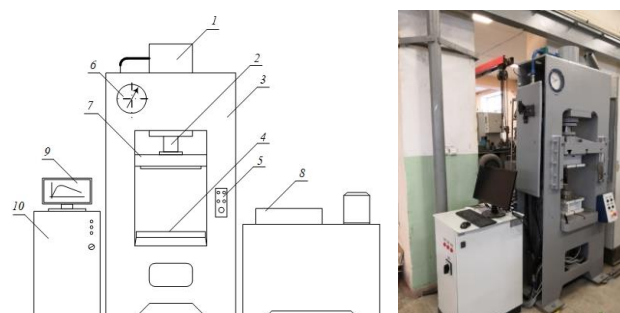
Схема и фото лабораторного гидравлического пресса: 1 – главный цилиндр; 2 – шток; 3 – станина; 4 – рабочий стол; 5 – пульт управления; 6 – манометр; 7 – ползун; 8 – маслостанция; 9 – монитор; 10 – блок управления и сбора данных
